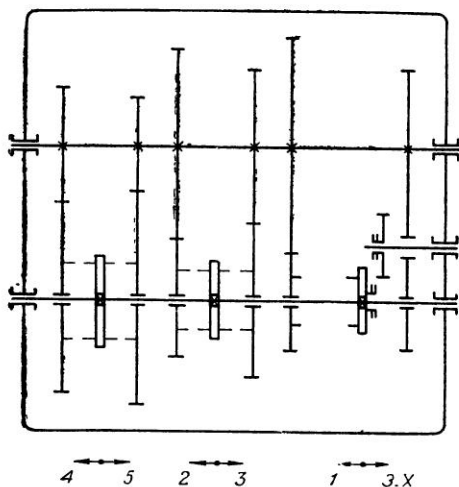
Схема пятиступенчатой коробки передач в блоке с главной передачей
